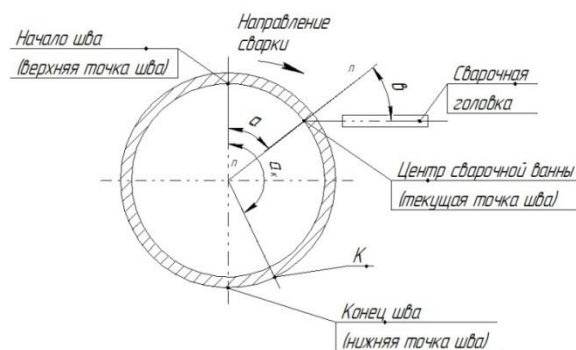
Расположение сварного шва на трубе.
